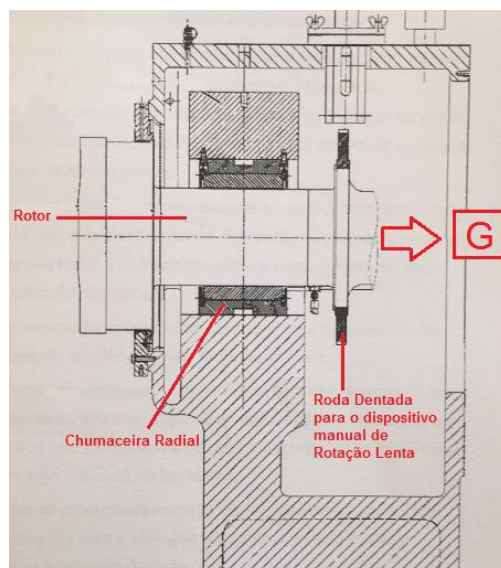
Vista de conjunto do apoio posterior do Rotor da Turbina [46]
